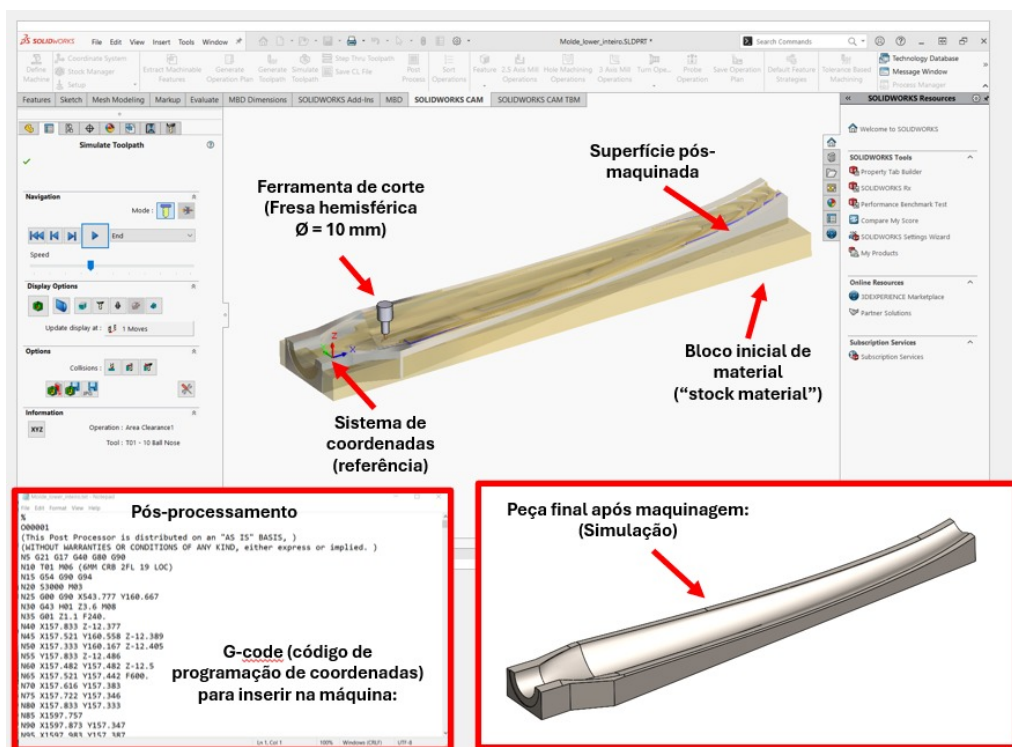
Configuração para a maquinação do molde da superfície inferior da pá
